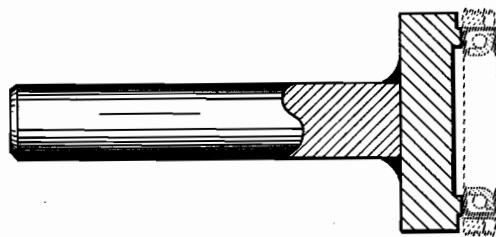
DEMONTAGE DU MOYEU AVANT
